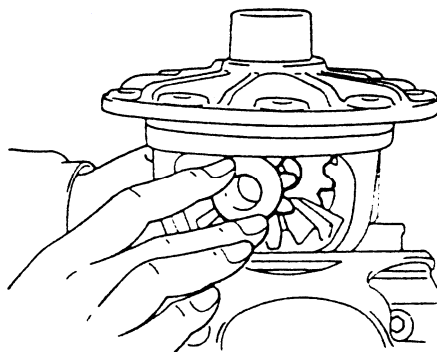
(c) 拆卸差速小齿轮及半轴齿轮
